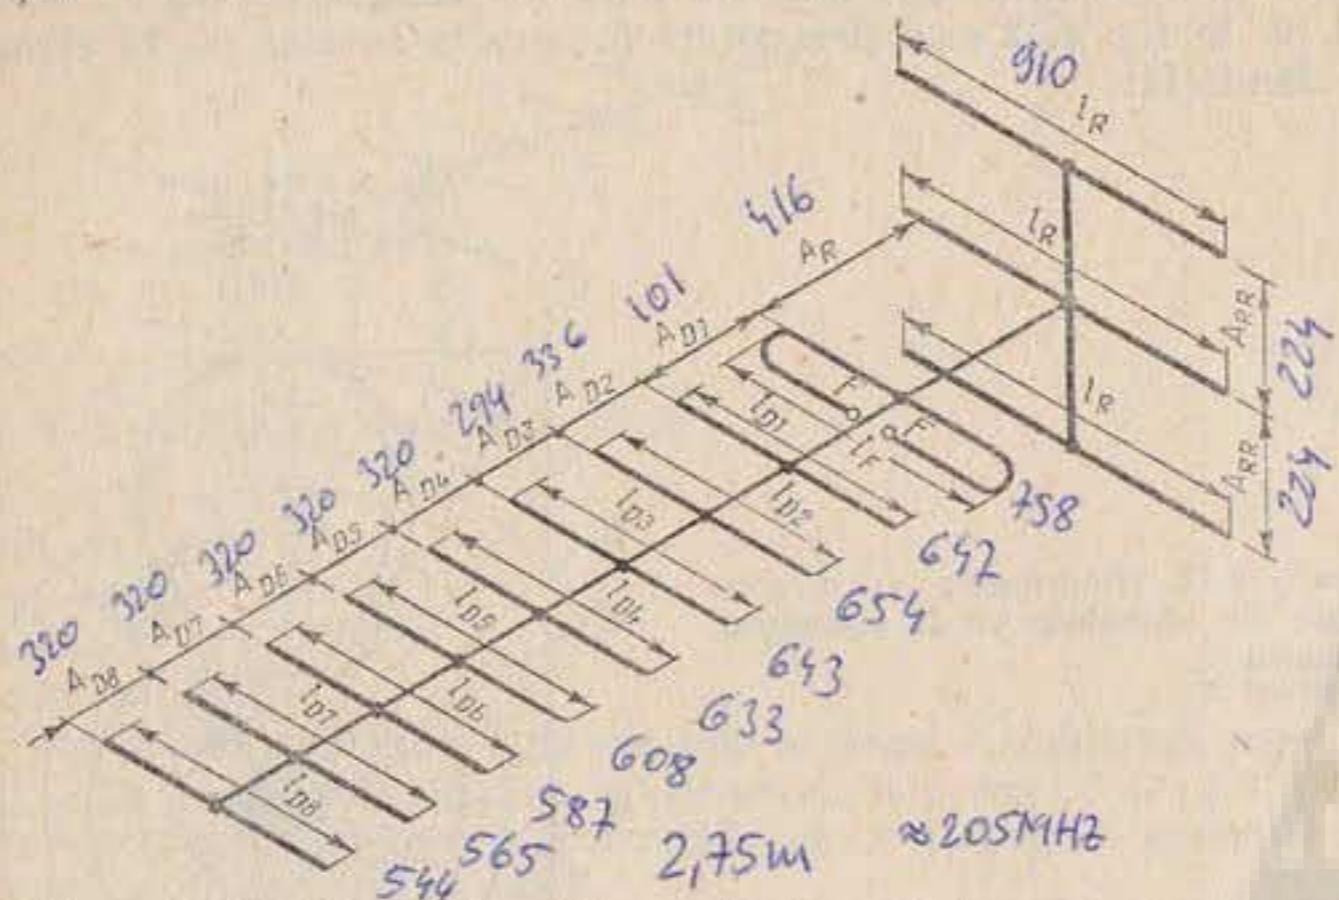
Schița constructivă a antenei cu 12 elemente.
